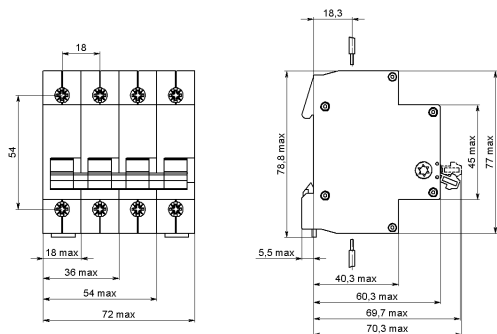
Габаритные, установочные, присоединительные размеры выключателей.
